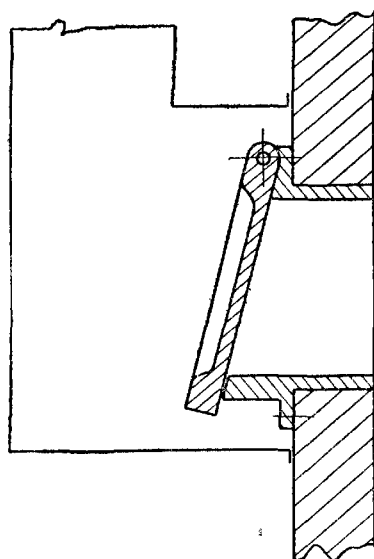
Взрывной клапан с закрывающейся крышкой.
